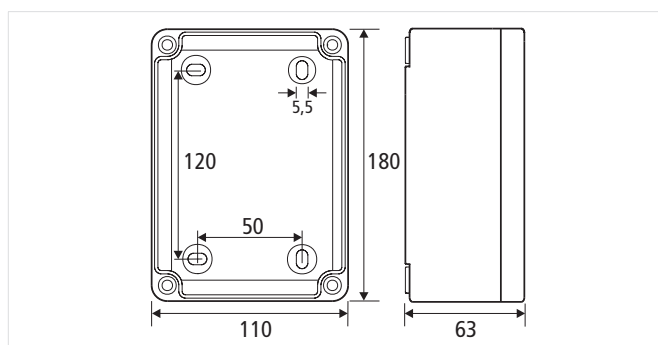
ADP-PRS-422-GEH, Draufsicht und Seitenansicht
